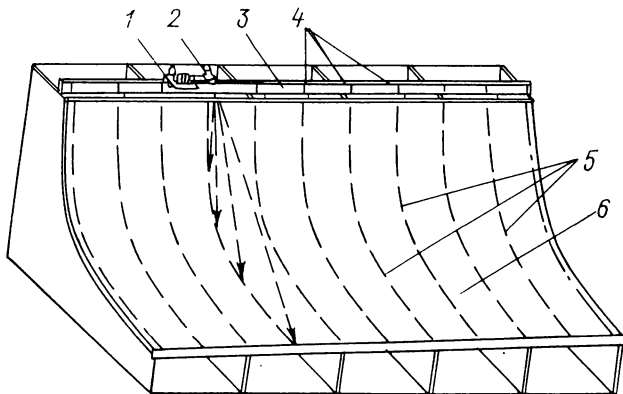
Схема разметки под установку набора лазерным разметчиком ЛАР-1 на каретке, перемещаемой по направляющей.
